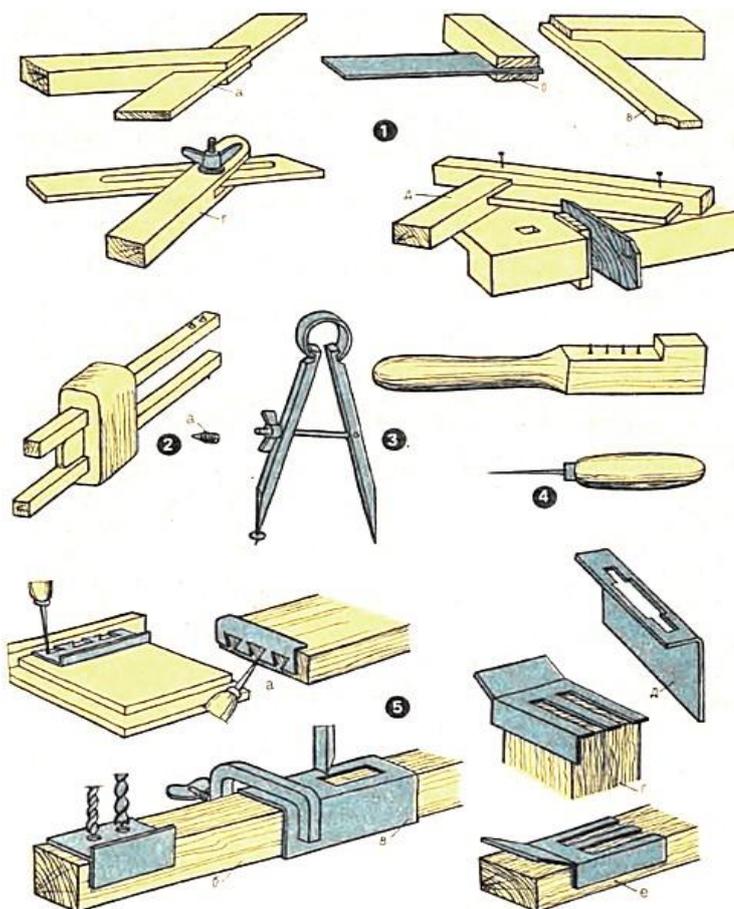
Разметочный и измерительный инструмент: 1 - угольники: а - рисунок (45°); б - прямой с металлическим пером; в - прямой с деревянным пером; г - малка универсальная; д - прием правки пера в верстаке;
